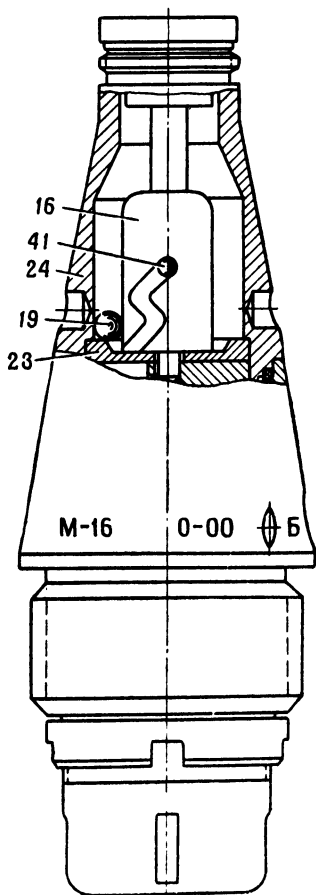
Положение деталей взрывателя при выстреле: 16 — оседающая гильза; 19 — верхний шарик; 23 — опорная втулка; 24 — головка; 41 — штифт
